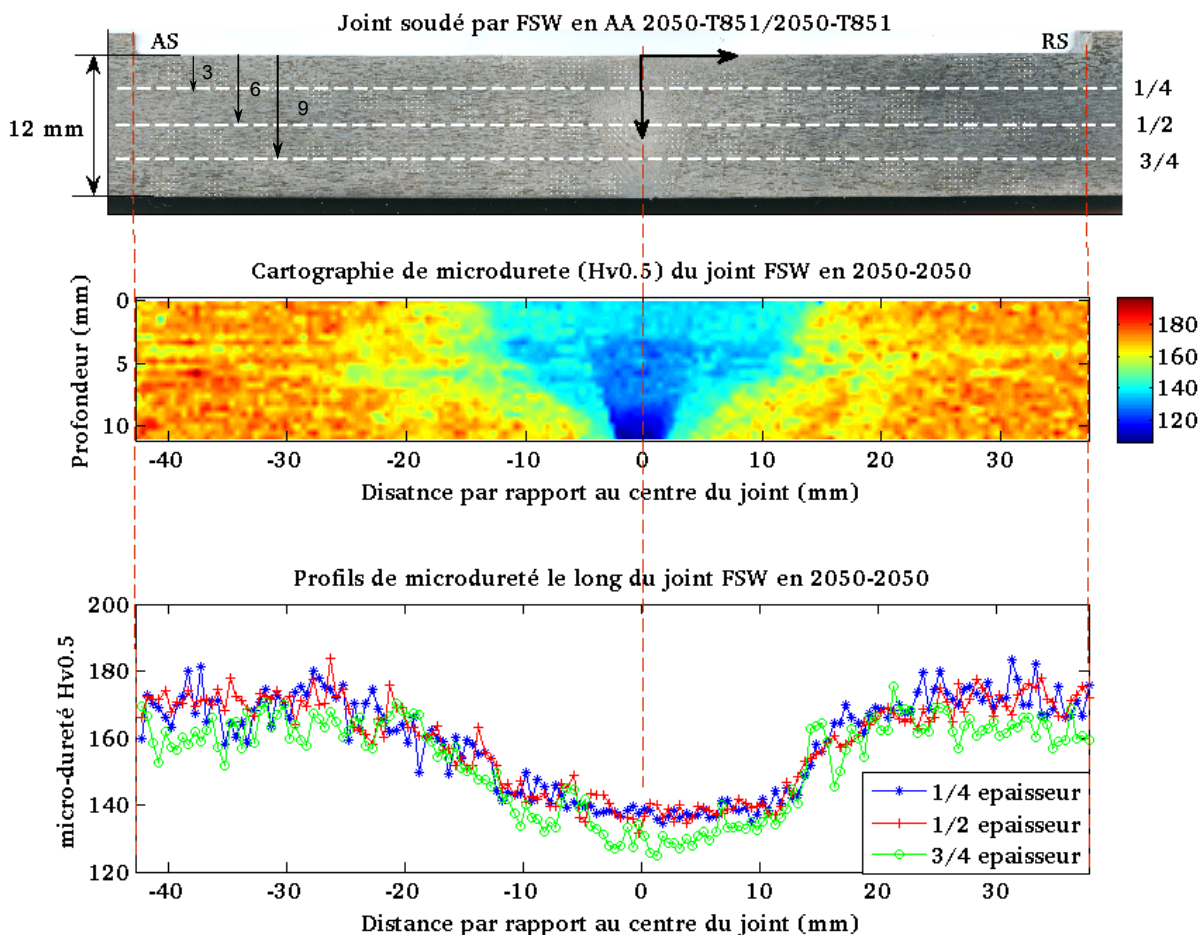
Cartographie de microdureté HV0.5 du joint soudé en alliage d'aluminium 2050-T851
